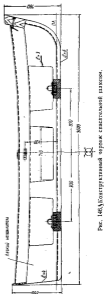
Конструктивный чертеж спасательной шлюпки.
